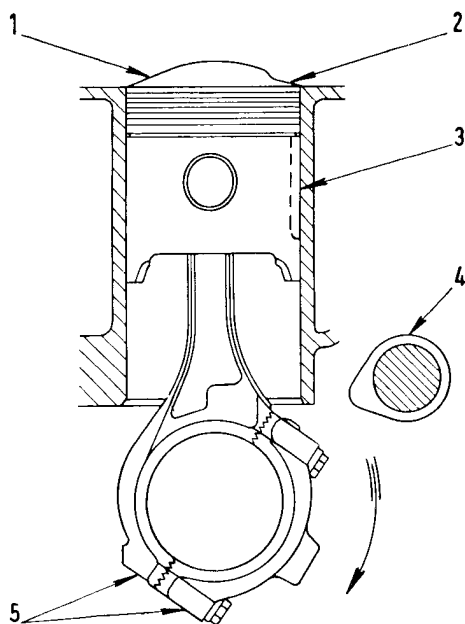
Schema per il montaggio del complesso biella-stantuffo nel cilindro.
